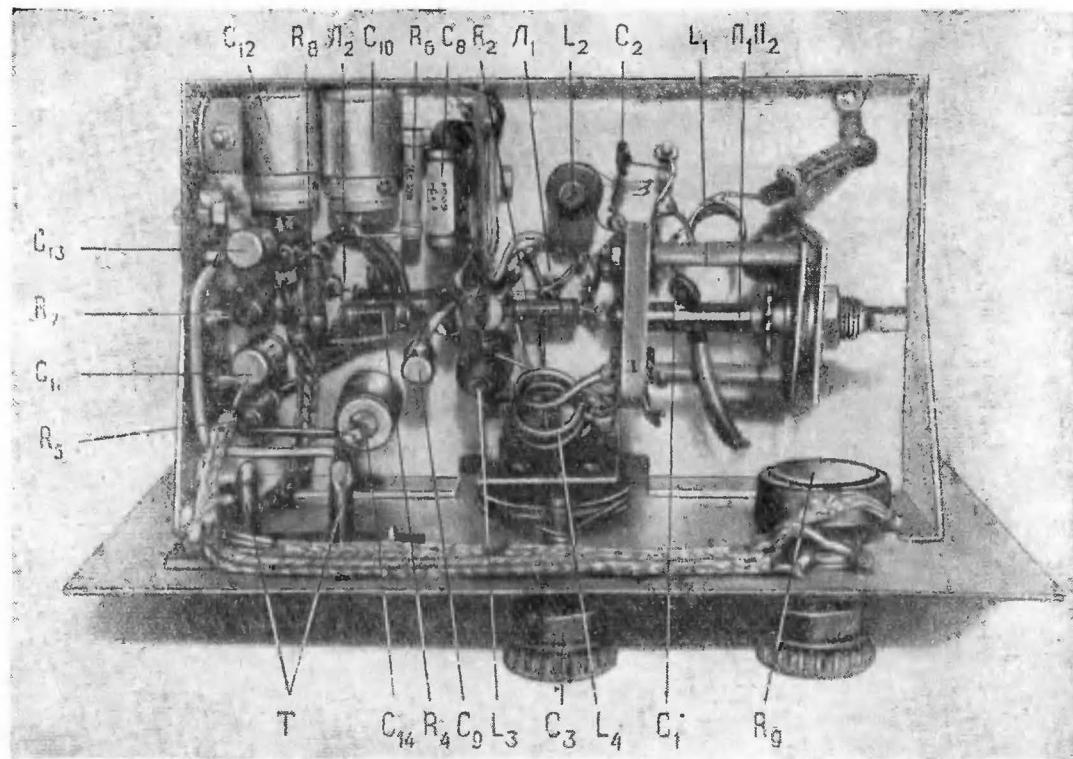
Расположение деталей и монтаж двухлампового сверхрегенеративного приемника.
